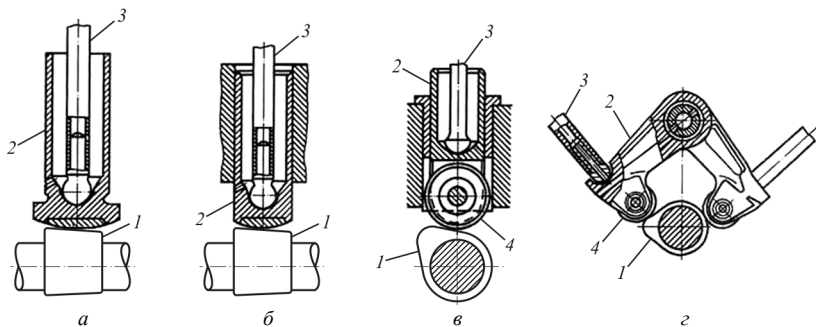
Типы толкателей: *а* – грибовидный; *б* – цилиндрический; *в* – цилиндрический роликовый; *г* – рычажный роликовый; 1 – кулачок распределительного вала; 2 – толкатель; 3 – штанга; 4 – ролик
